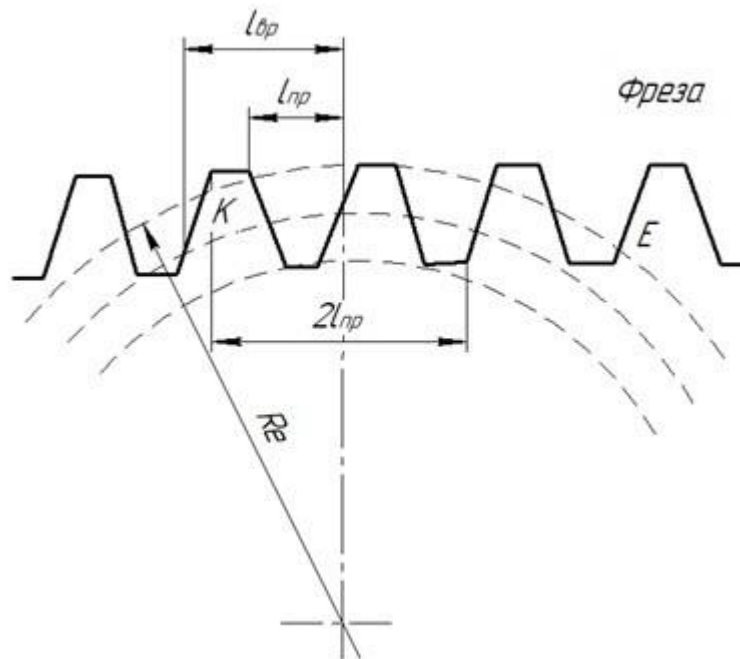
Схема контролю довжини черв'ячної зуборізної фрези
